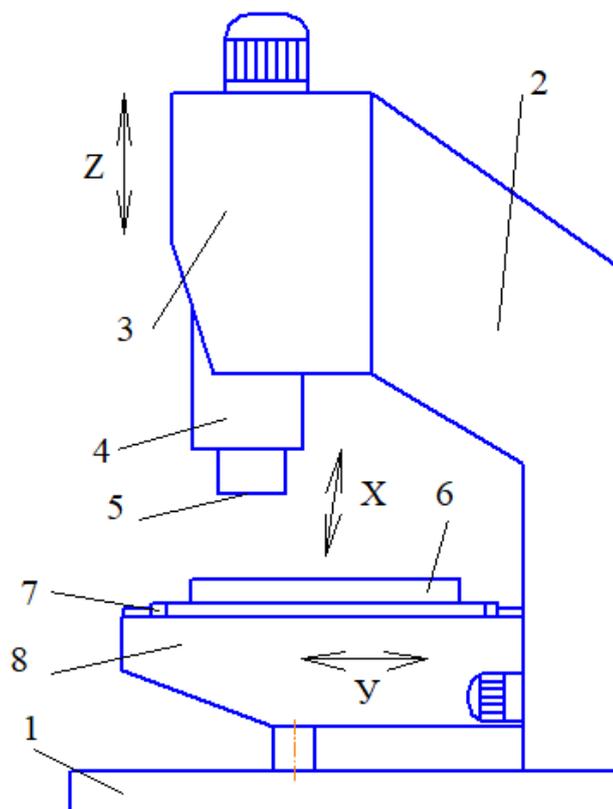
Компоновка консольного вертикально-фрезерного станка с ЧПУ
